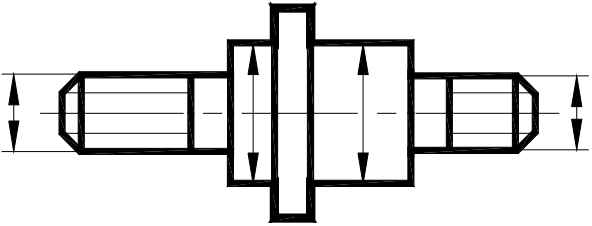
Нанесение размеров на чертеже стандартной крепёжной детали
